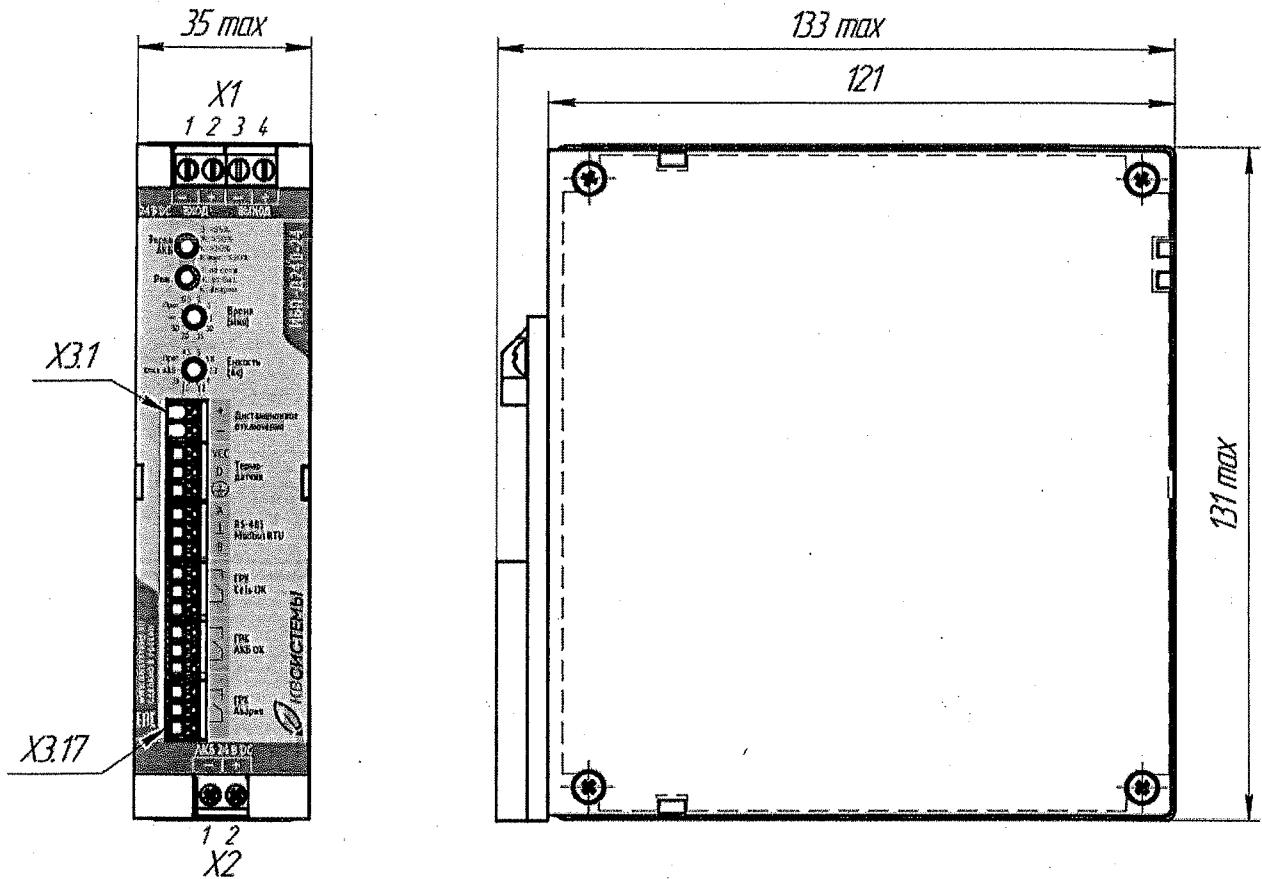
Внешний вид и габаритные размеры изделия ИБП-Д240-24
